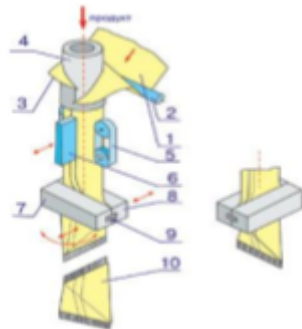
Технологічна схема машини для пакування сипких матеріалів – плівка; 2 – натяжний валок; 3 – форма комірець; 4 – продуктопровід; 5 – механізм протягування; 6 – губки поздовжнього зварювання; 7 і 8 – губки поперечного зварювання; 9 – відрізнальний механізм; 10 – готовий пакет
